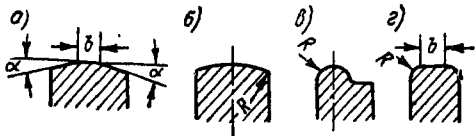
Формы рабочего профиля роликов при обкатывании поверхностей.
